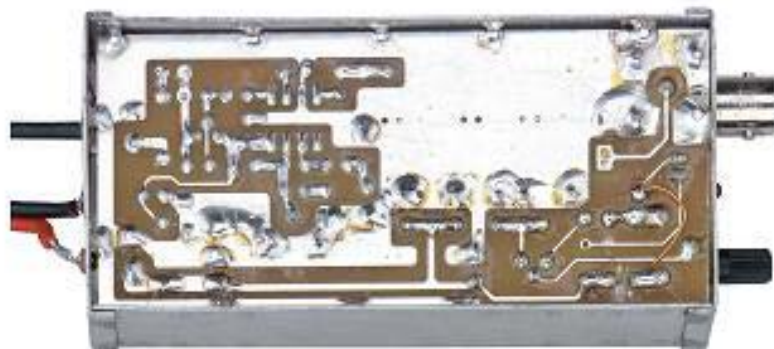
El circuito impreso ha de soldarse a la carcasa metálica del mueble por ambos lados.
